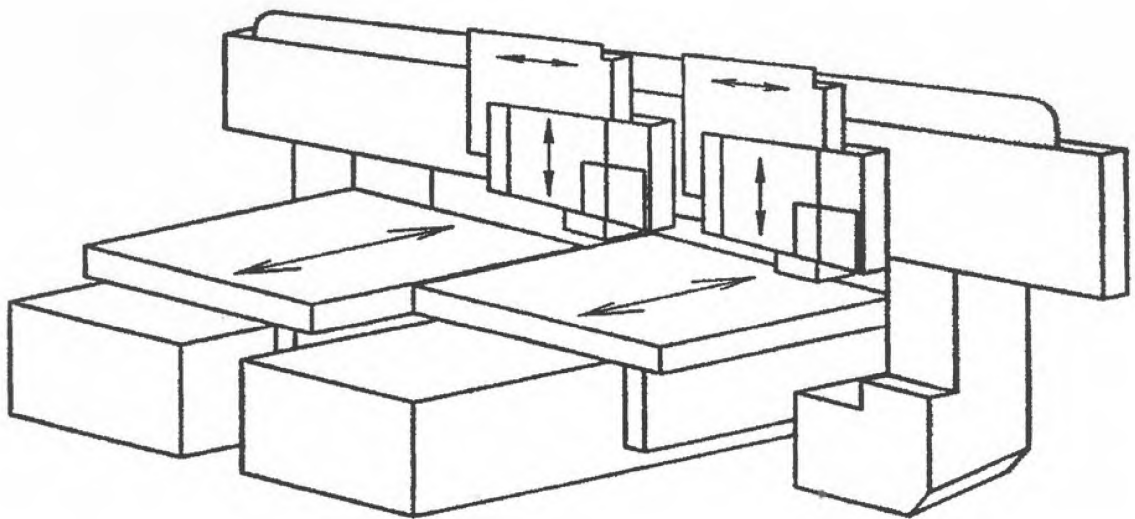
Фрезерный станок с верхним расположением шпинделя (подвижный стол, неподвижный портал, подвижная головка)¹
